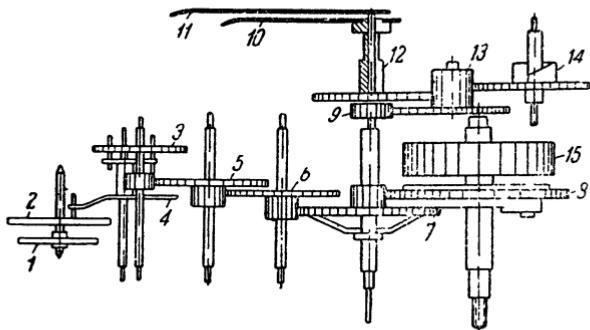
Схема работы механизма хода и стрелочного механизма будильника: 1—волосок; 2—балансовое колесо; 3—анкерное колесо; 4—вилка; 5—секундное колесо; 6—промежуточное колесо; 7—среднее колесо; 8—узел заводного колеса; 9—минутник; 10—часовая стрелка; 11—минутная стрелка; 12—часовое колесо; 13—вексельное колесо; 14—сигнальное колесо; 15—заподная пружина хода
